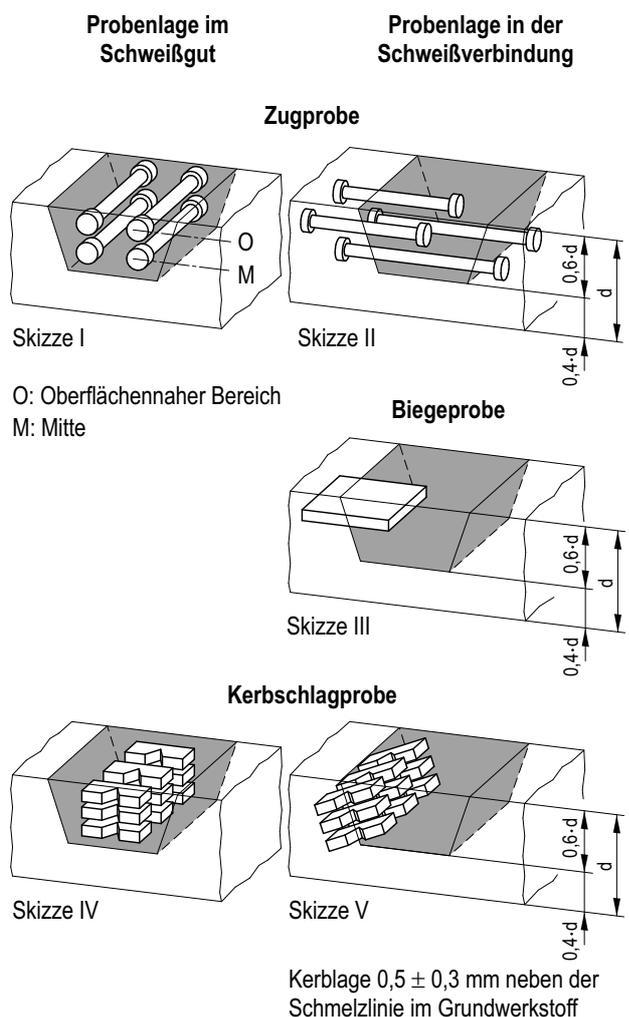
Probenentnahme bei Verfahrensprüfungen für Ausmuldungsschweißungen
